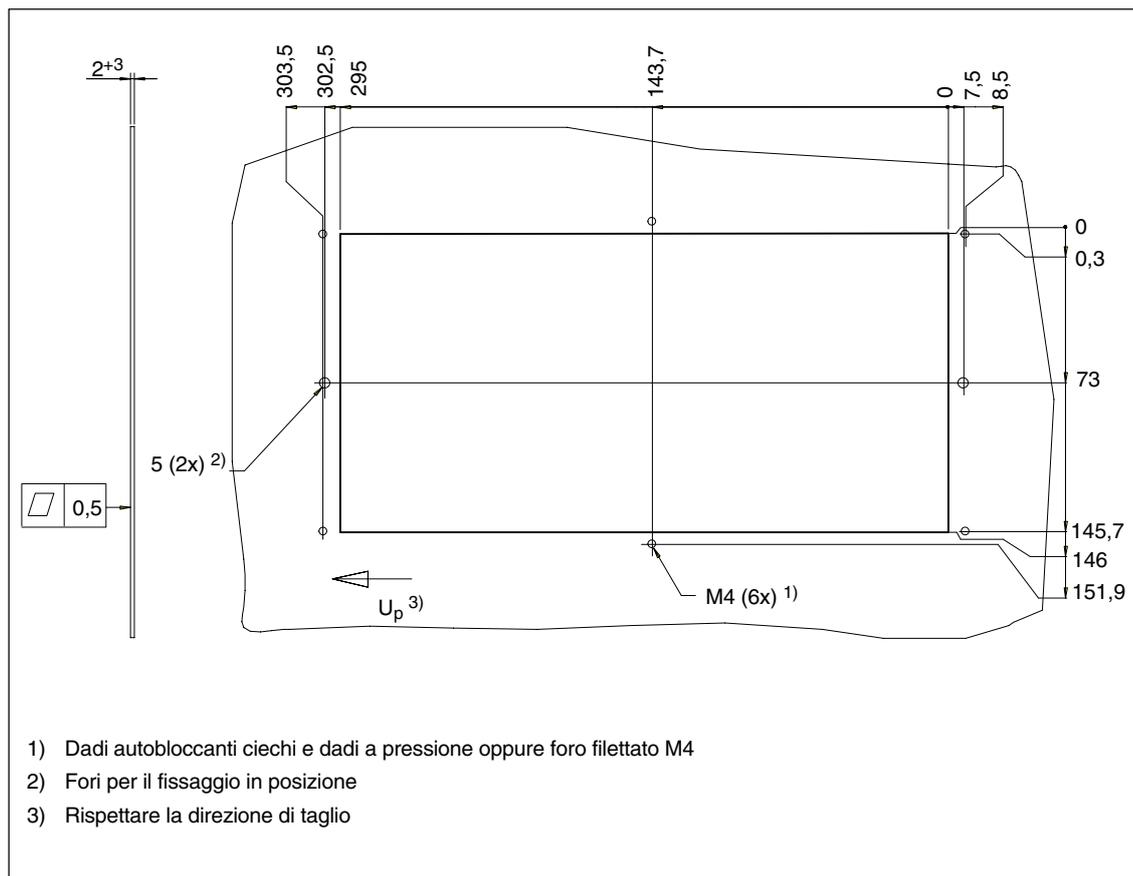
Schema di foratura per la tastiera CN (montaggio accanto alla PCU)
